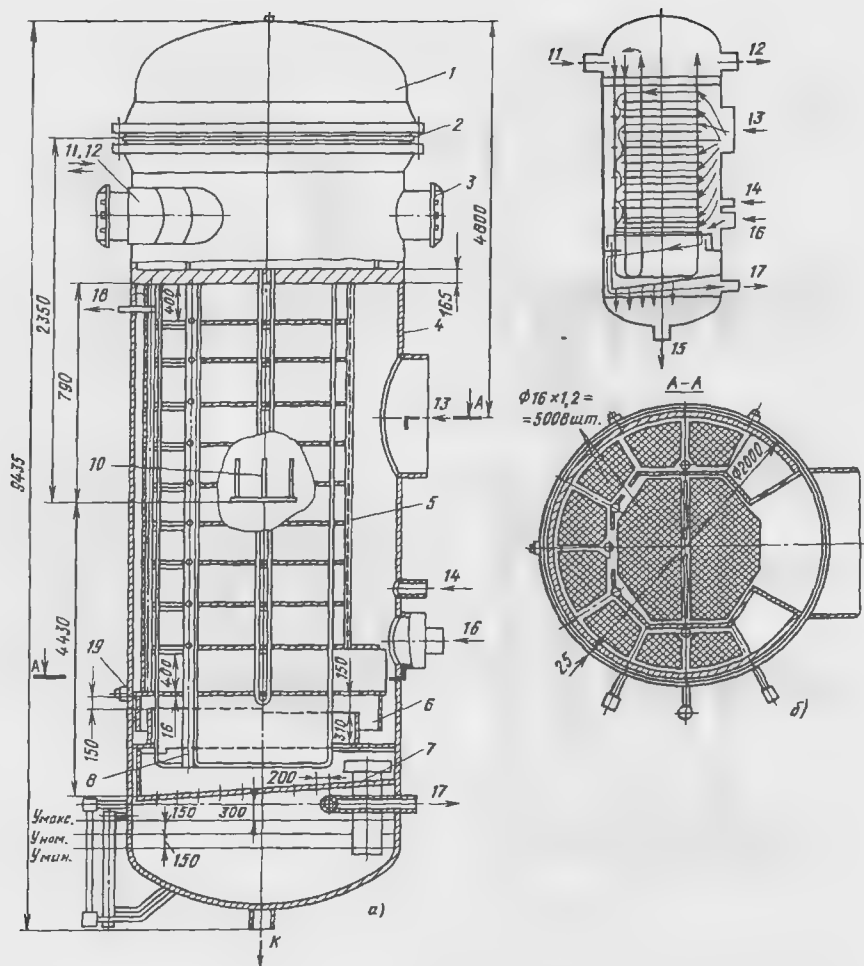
Подогреватель низкого давления ПН-2300-25-7-IV:
